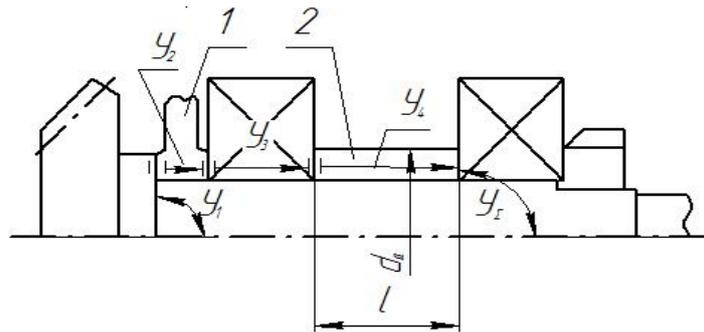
Схема базирования подшипника через промежуточное кольцо и короткую ступицу
